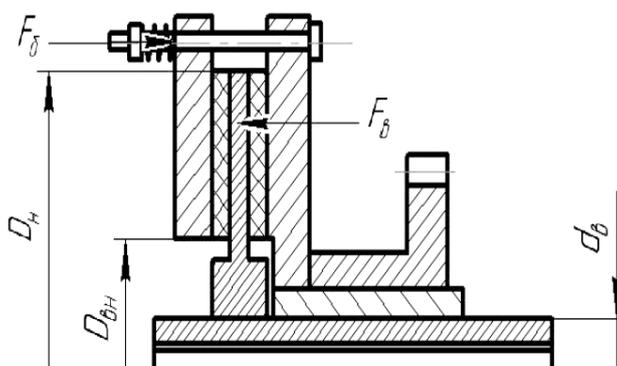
Конструктивные размеры предохранительной муфты
